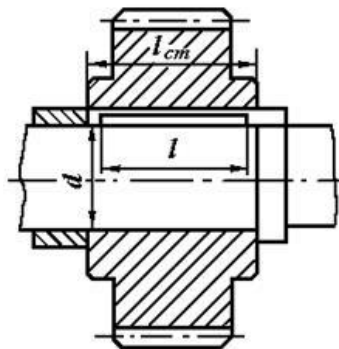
Шестерня, закрепленная на валу призматической шпонкой
